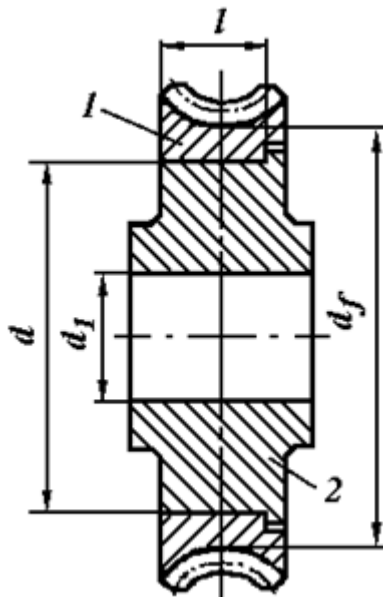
Цилиндрическое соединение с натягом венца червячного колеса с центром
